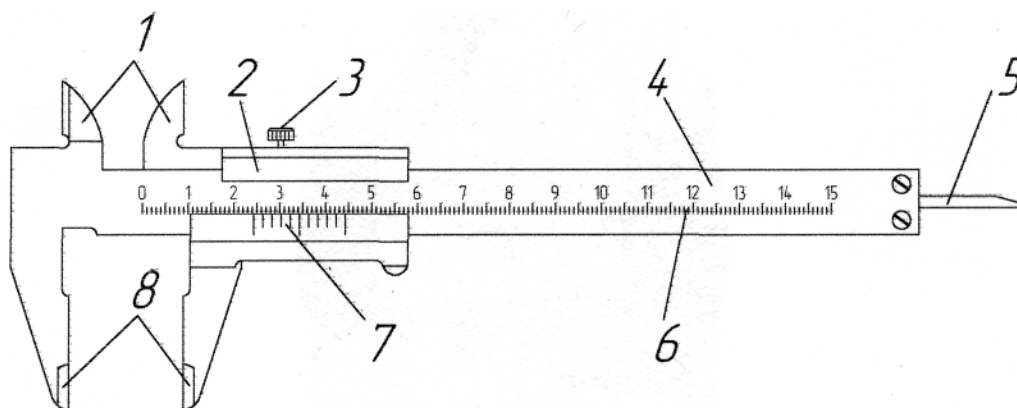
Штангенциркуль ШЦ-I двусторонний с глубиномером: 1 - губки для внутренних измерений, 2 - рамка, 3 - зажим рамки, 4 - штанга, 5 - линейка глубиномера, 6 - шкала штанги, 7 - нониус, 8 - губки для наружных измерений
